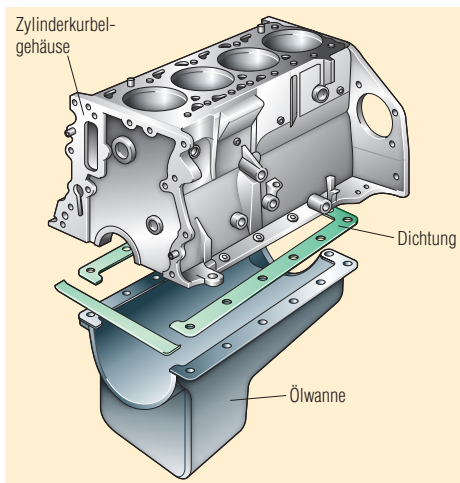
Zylinderkurbelgehäuse mit Ölwanne.
